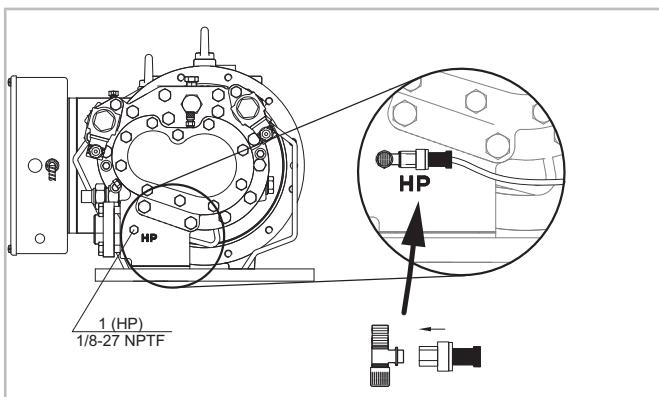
HS.64-Verdichter: Montage des Hochdruckmessumformers
